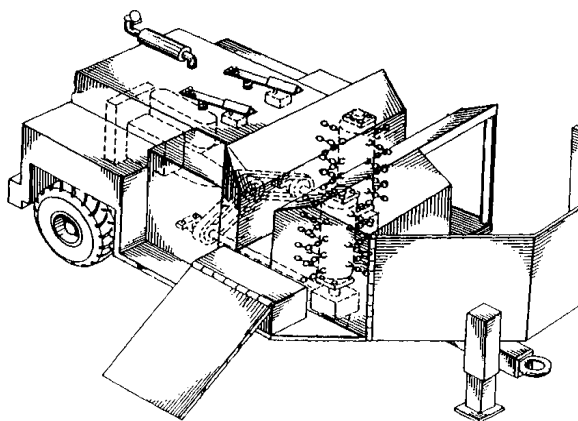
Вертикальный окорочный станок VFDD-1642 [108]
